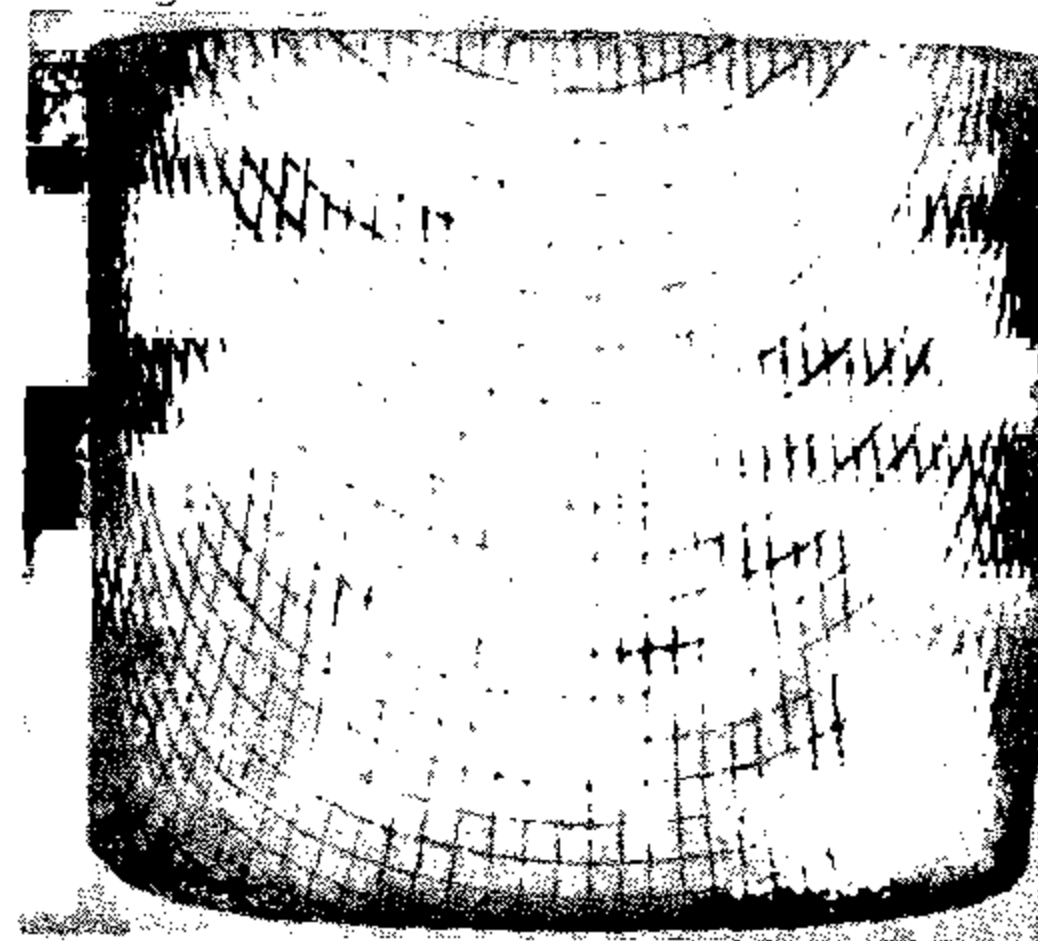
Перемещение сетки на боковую поверхность стенки большого диаметра овала
